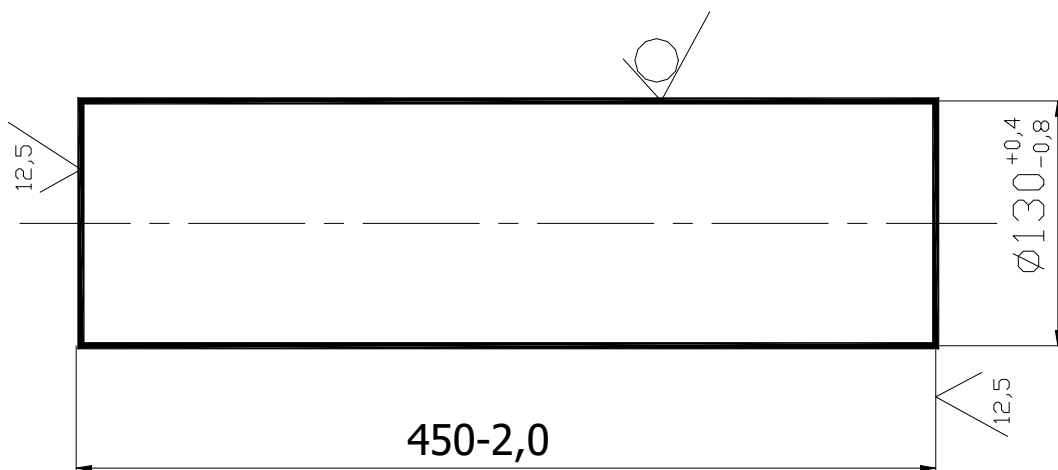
Ескіз заготовки із круглого прокату
